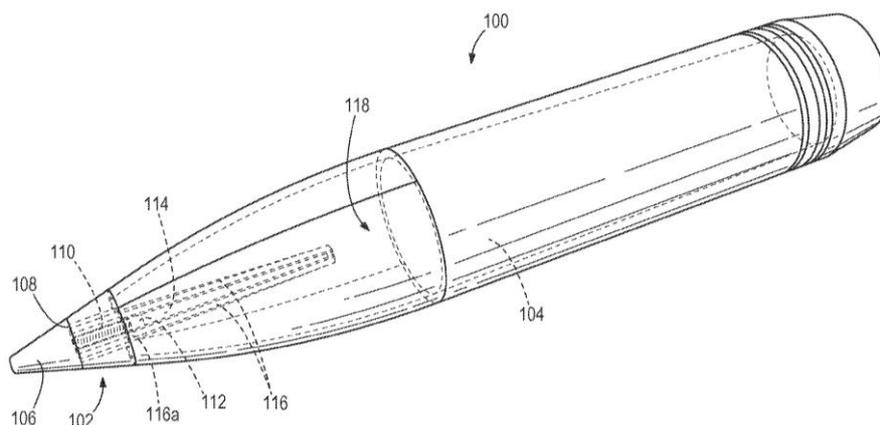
Proyectil extintor de apertura delantera, vista exterior. Fuente:[17]
